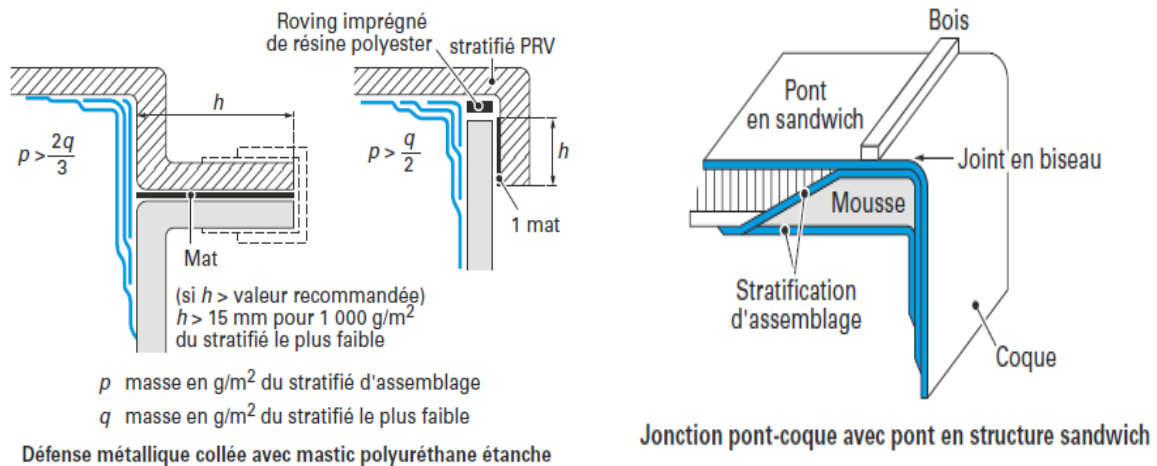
Assemblage par collage en construction navale : pont-coque [16].
